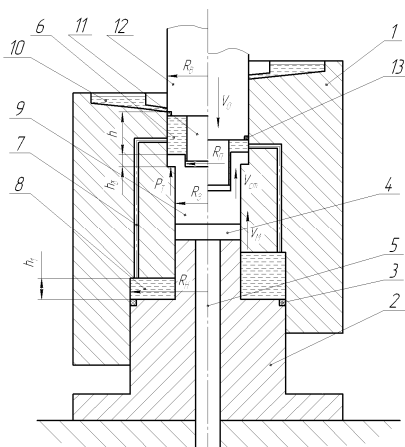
Схема штампу для видавлювання з розтягом сталевих виробів з порожниною постійного діаметра
